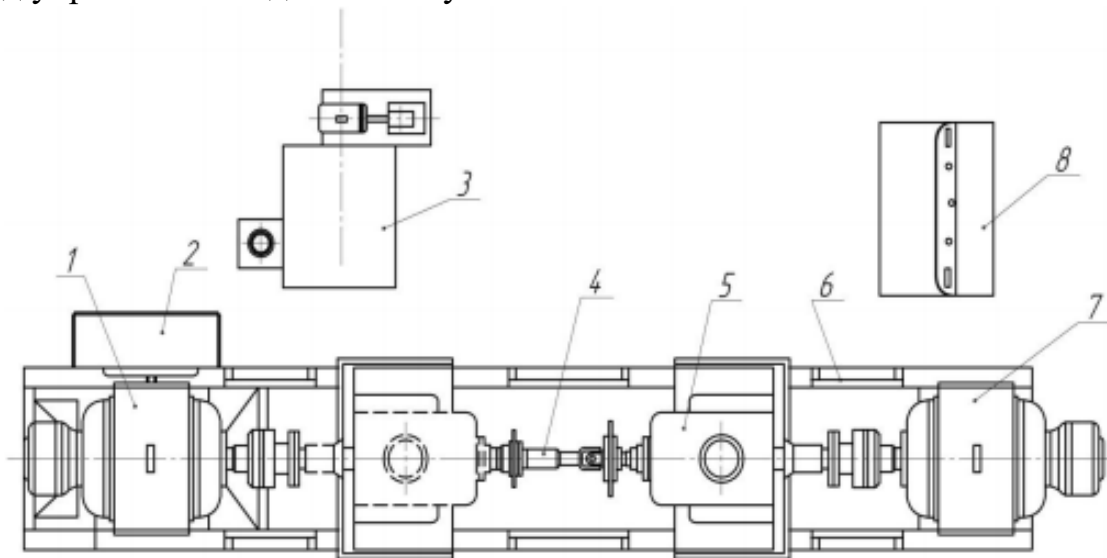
3 Стенд для коробок передач модель 6101-11
